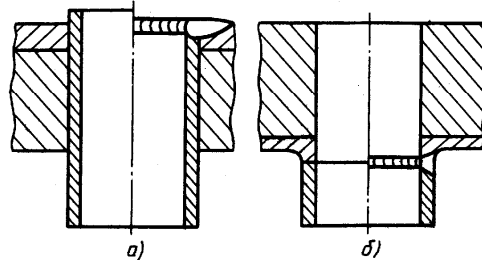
Схемы сварки труб с биметаллическими трубными решетками
